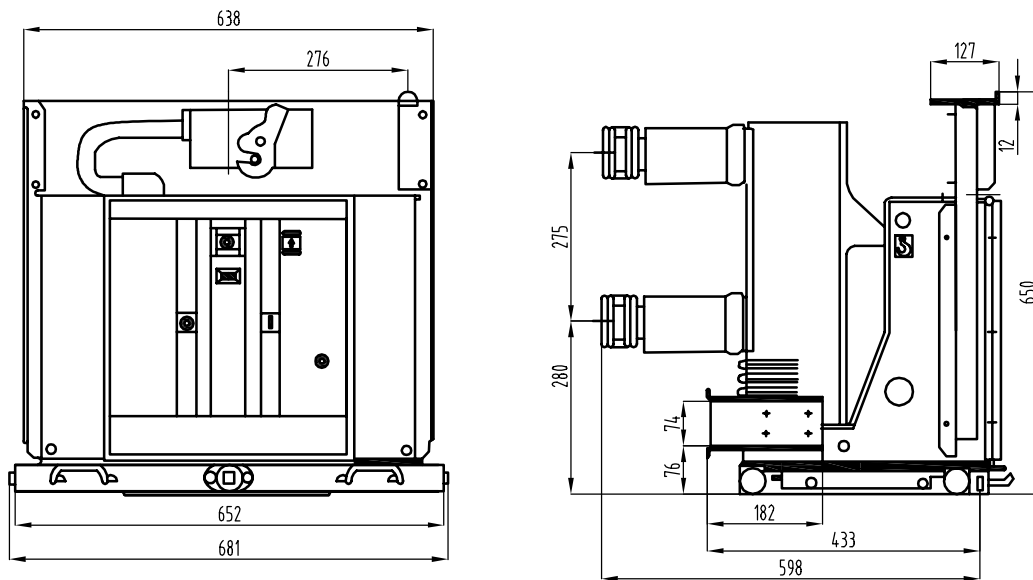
Габаритный размер выключателя ВВ-12 выкатного исполнения для ячейки шириной 800 мм
